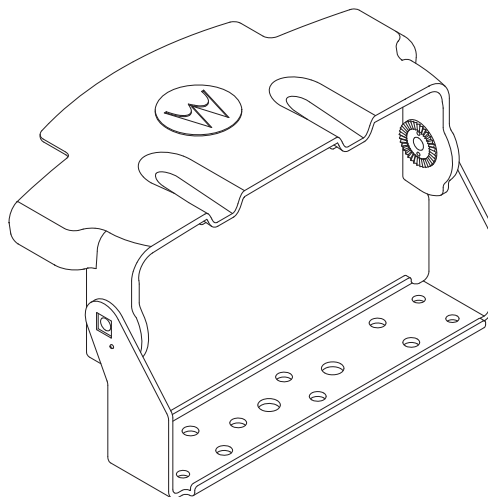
Munhão de Montagem Remota com Protetor Solar
